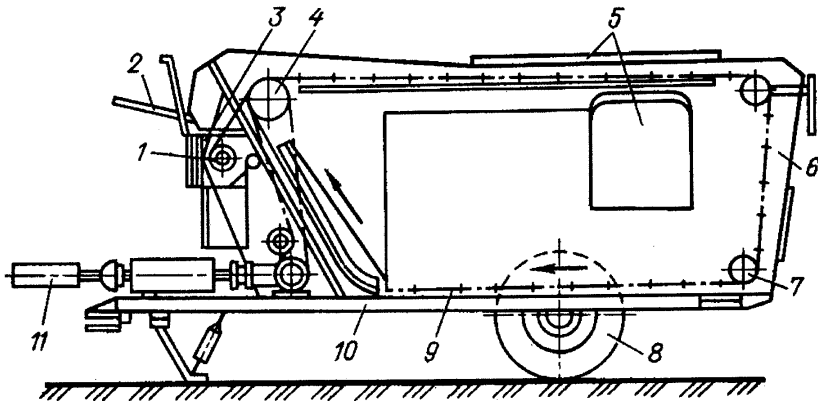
Схема кормороздавача КУТ-3,0А: 1-розвантажувальний шнек; 2-важіль повороту заслінки; 3-вивантажувальний пристрій; 4-приводні зірочки; 5-завантажувальні вікна; 6-бункер; 7-зірочки; 8-ходова частина; 9- ланцюгово-планковий транспортер; 10-рама; 11-вал відбору потужності.
